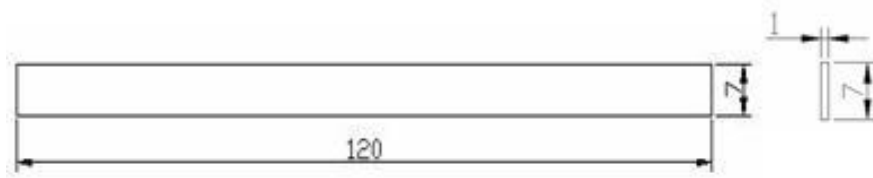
Dimensões do corpo de prova laminado em mm, para ensaios mecânicos.
